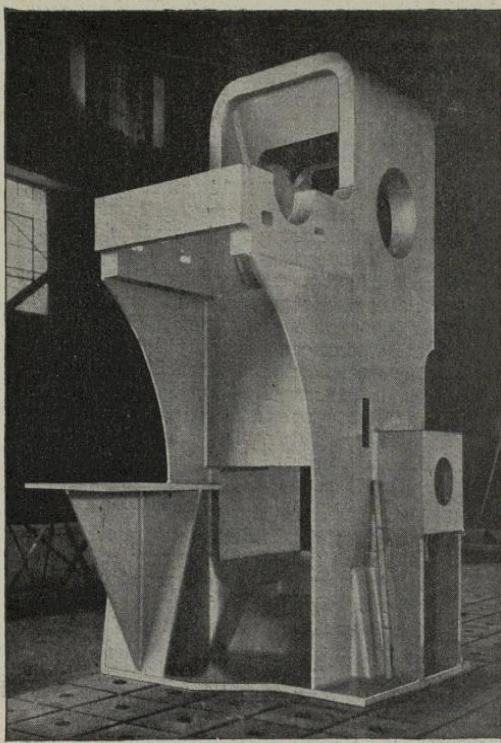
Vue arrière du bâti de presse soudé électriquement, représenté sur la figure de tête.
